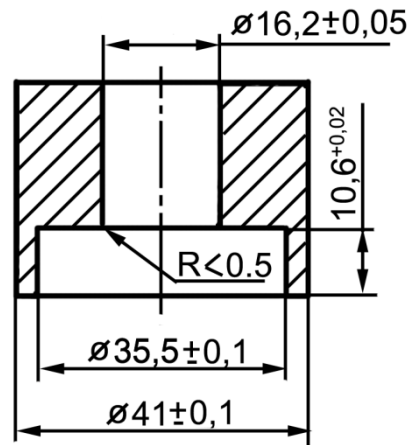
Оправка для запрессовки уплотнения водяного насоса (Основные конструктивные размеры)
